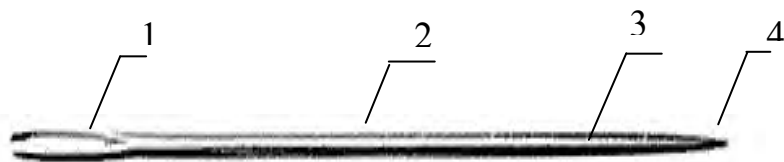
Типовая конструкция иглы из проволочной заготовки:
